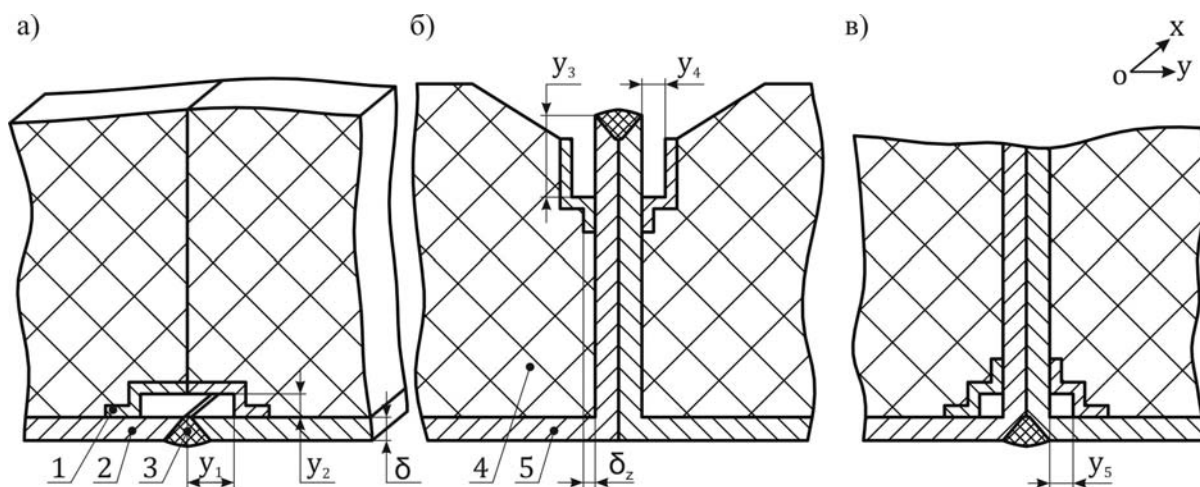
Расчетные случаи сварных монтажных стыков: 1 – защитный элемент; 2 – формообразующий лист; 3 – сварное соединение монтажного стыка; 4 – заполнитель; 5 – формообразующий лист с отбортовкой
